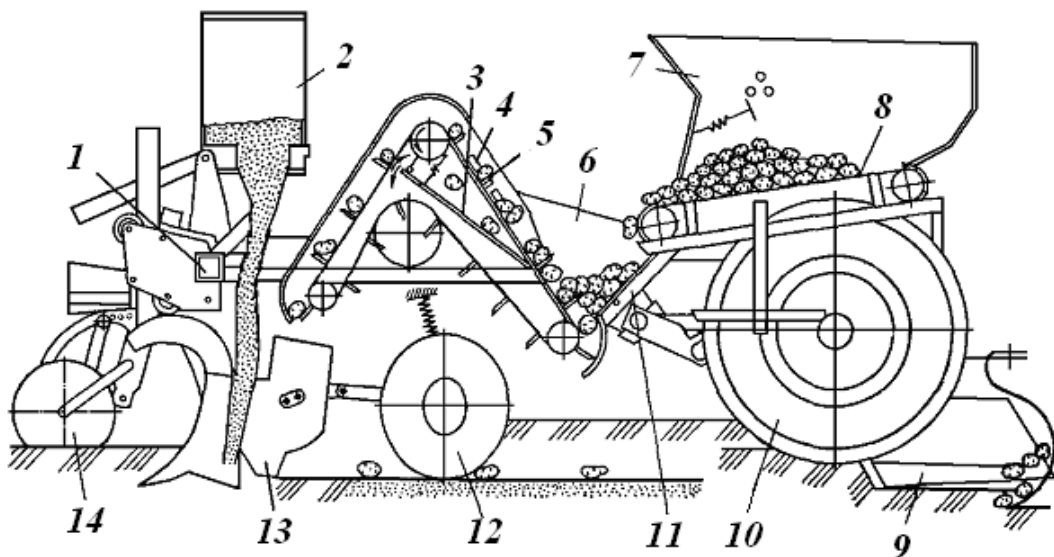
Схема картоплесаджалки САЯ-4: 1 - рама; 2 - туковисівний апарат; 3 - потік; 4 - пружина; 5 - ложечка садильного апарата; 6 - живильний ківш; 7 - бункер; 8 - конвеєр бункера; 9 - розпушувальний пристрій; 10 - ходове колесо; 11 - клапан з пристроєм; 12 - диск; 13 - сошник; 14 - опорне колесо сошника.
